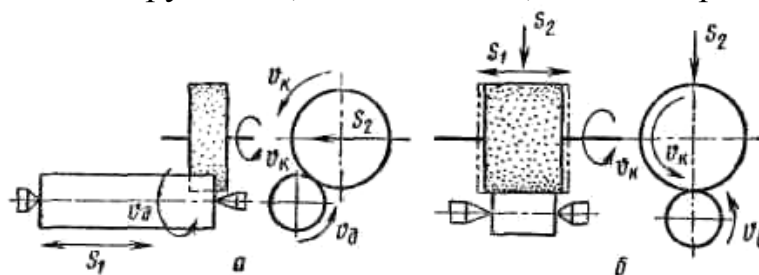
Схемы взаимодействия инструмента и заготовки на круглошлифовальных станках
